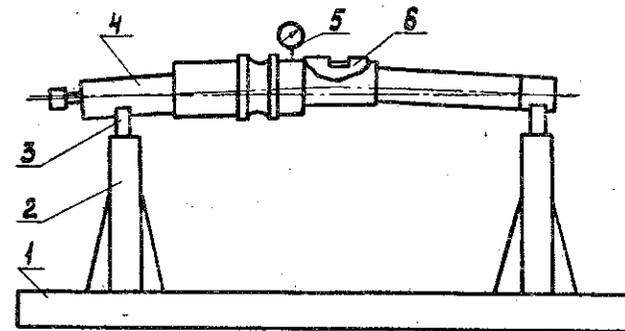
Приспособление для термической правки валов: 1-основание; 2-стойка; 3-упор призматический с латунной подкладкой; 4-вал; 5-индикатор; 6-асбестовый лист с прямоугольным отверстием
